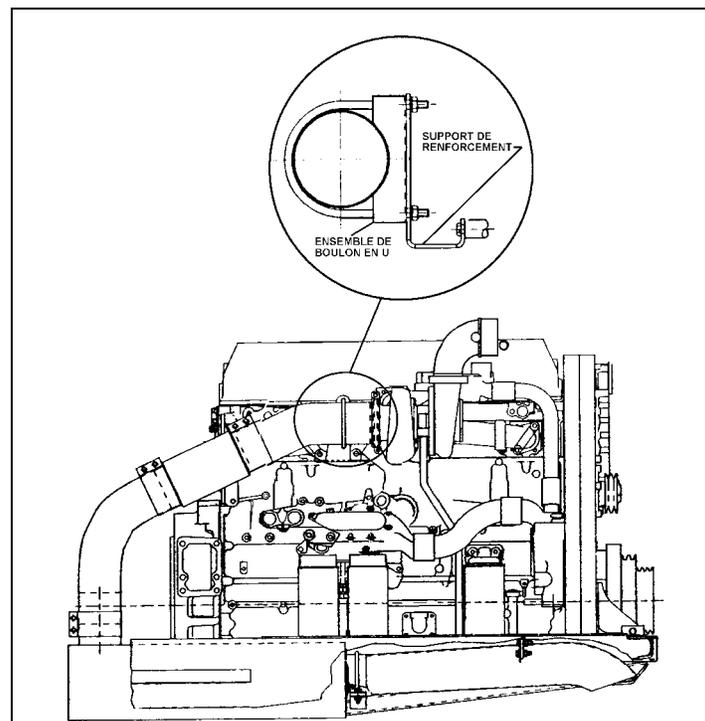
VUE DU MOTEUR - CÔTÉ TURBOCOMPRESSEUR
